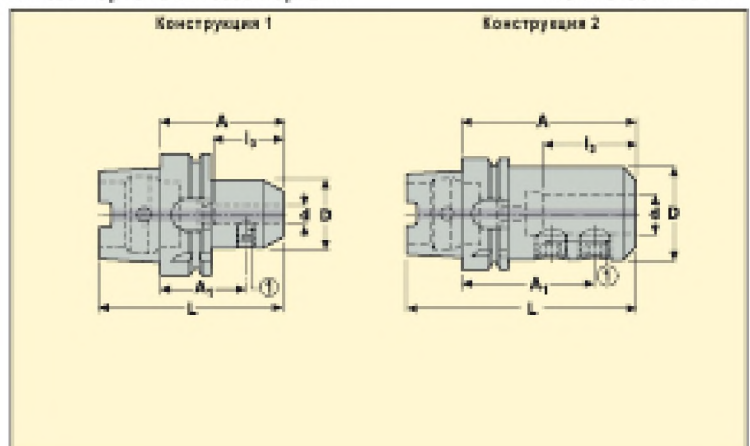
Патрон HSK-A з боковим затиском, Weldon – DIN 6535
